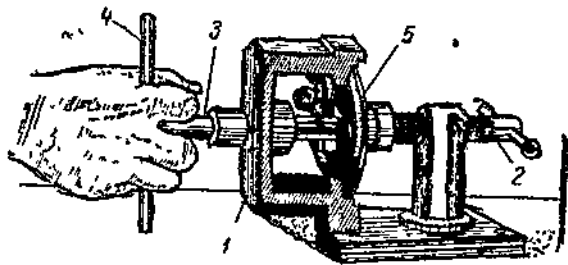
Приспособление для обработки внутренней поверхности втулки подшипника
